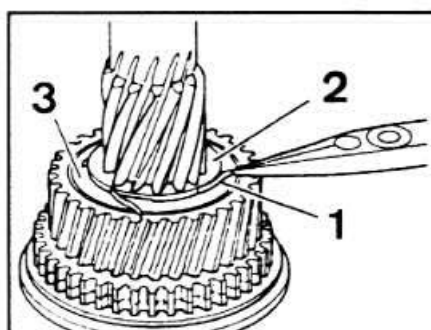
Отгибание язычков запорного кольца шестерни IV передачи:
